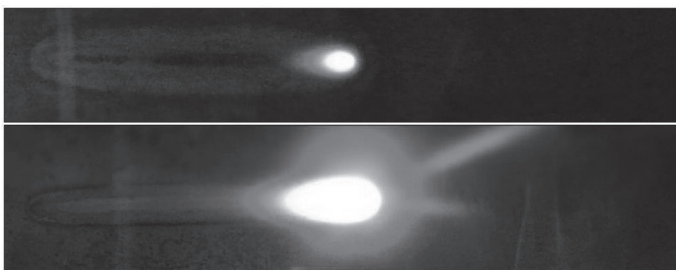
Raiz do cordão durante o processo de soldagem TIG CC- com parâmetros de soldagem: $L_a = 3$ mm, $V_s = 20$ cm/min., proteção gasosa argônio puro e (a) 100 A e (b) 150 A
